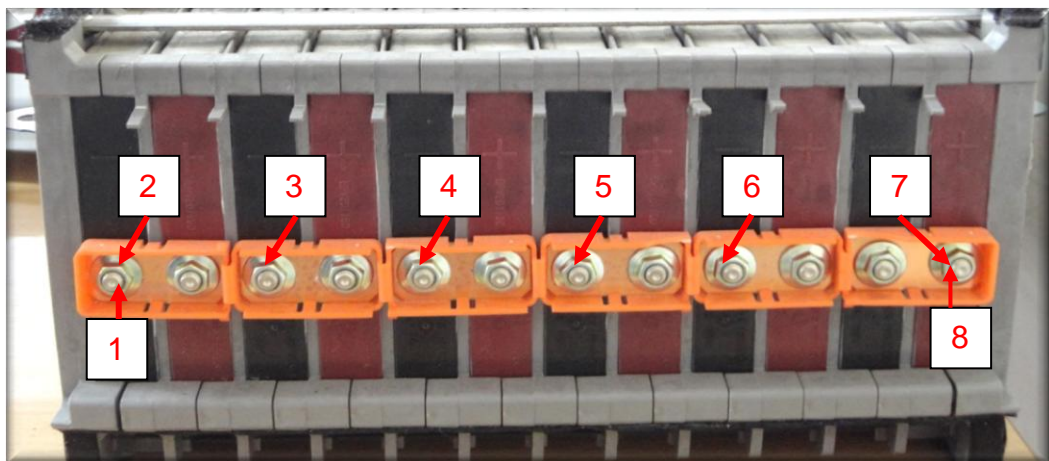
Conexión del bloque de la batería al dispositivo.
